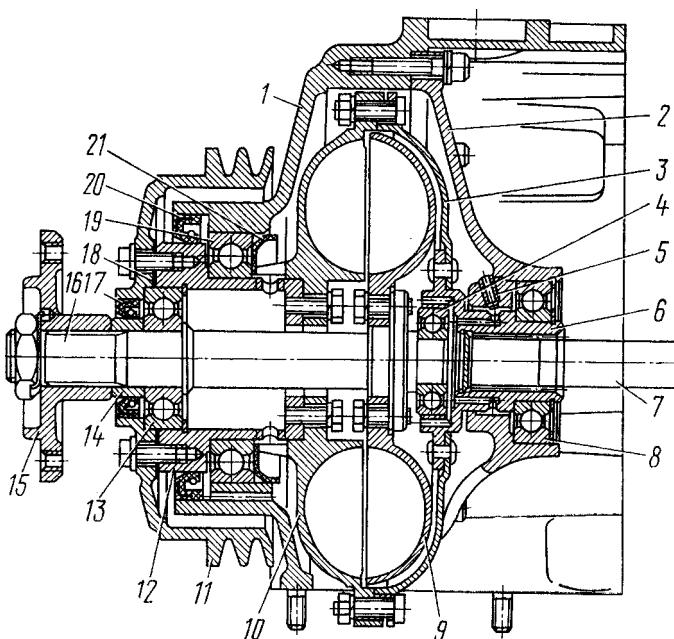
Гидромуфта привода вентилятора: 1 - крышка передняя; 2 - корпус подшипника; 3 - кожух; 4, 8, 13, 19 - подшипники шариковые; 5 - трубка корпуса подшипника; 6 - вал ведущий; 7 - вал привода гидромуфты; 9 - колесо ведомое; 10 - колесо ведущее; 11 - шкив; 12 - вал шкива; 14 - втулка упорная; 15 - ступица вентилятора; 16 - вал ведомый; 17, 20 - манжета с пружинами; 18 - прокладка; 21 - маслоотражатель
